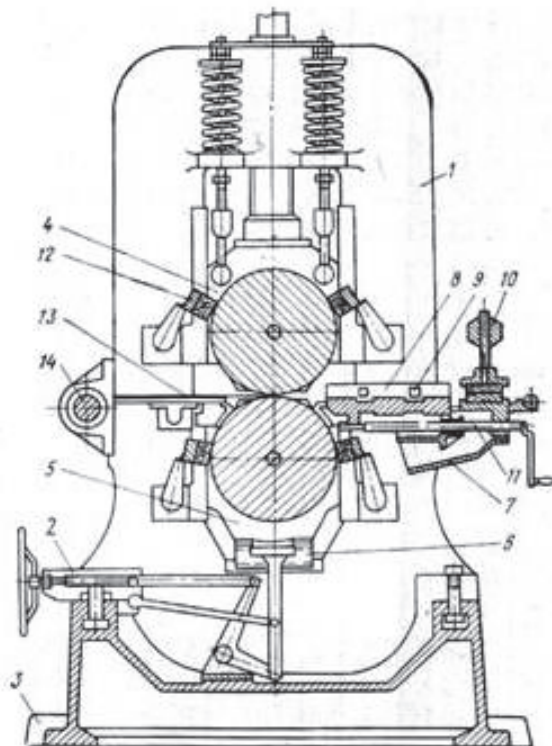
Рабочая клеть двухвалкового прокатного стана
